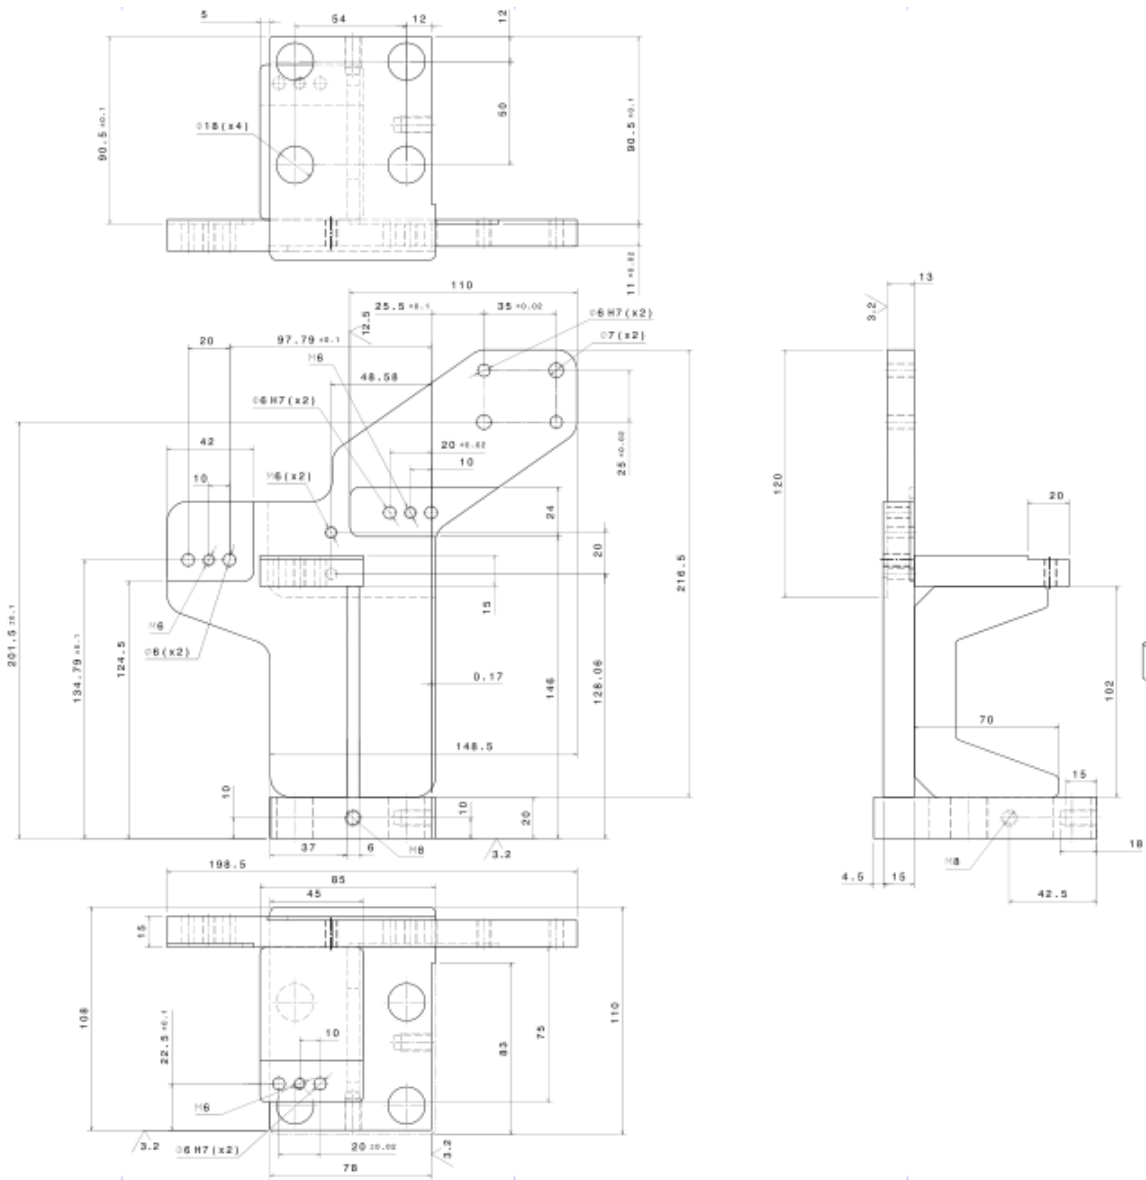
Plano de soldadura de un poste mecosoldado. Posteriormente a la soldadura se mecanizará en la fresadora. Fuente: Interob (2016).
